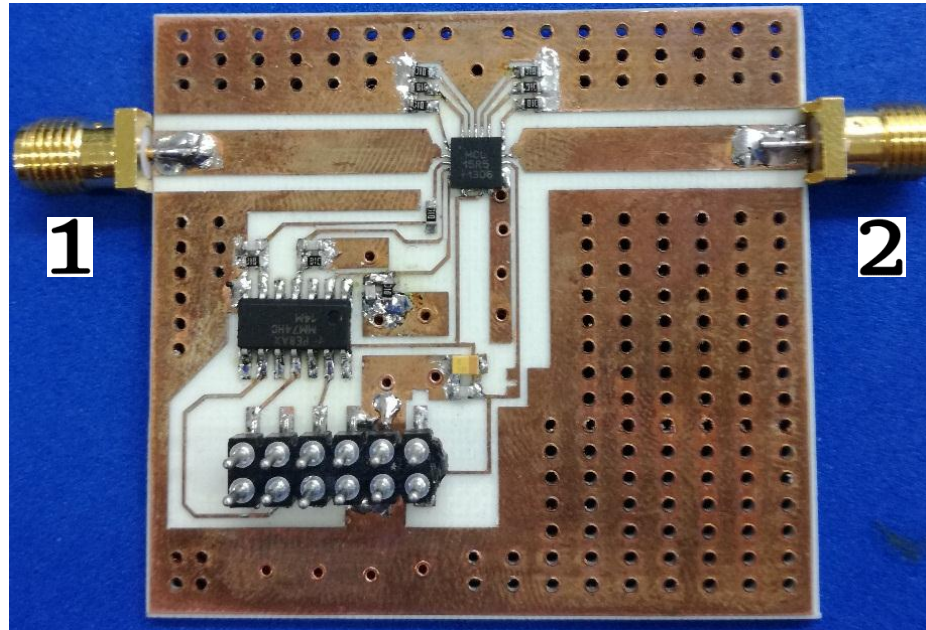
PCB fabricada a partir del diseño propuesto para el DAT-15R5A-SP+.
